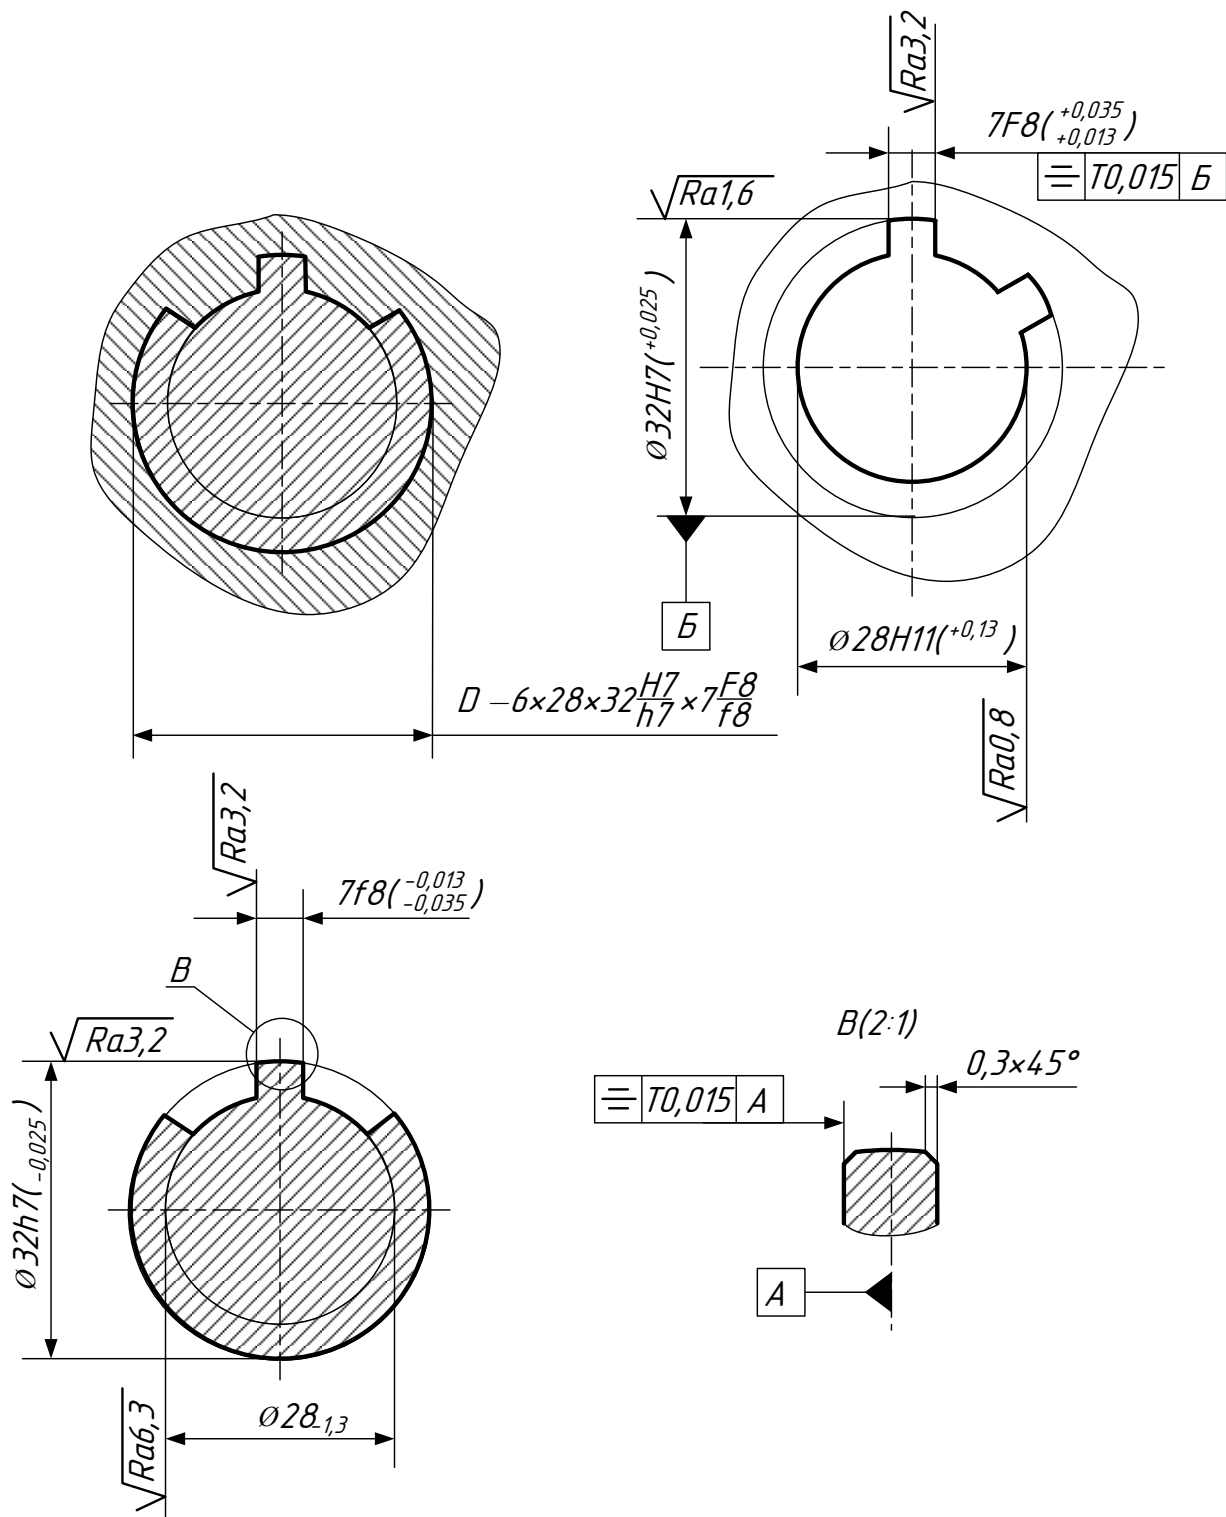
Эскизы шлицевого соединения и деталей
